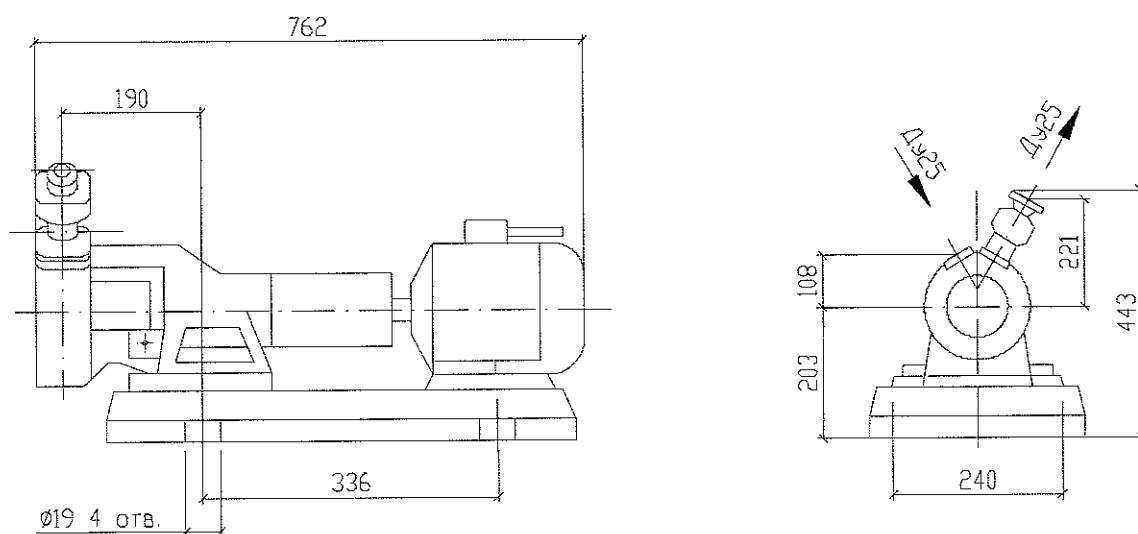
Габаритный чертеж насоса откачки бака сбора протечек топлива ВКС-1/16Б-2Г
